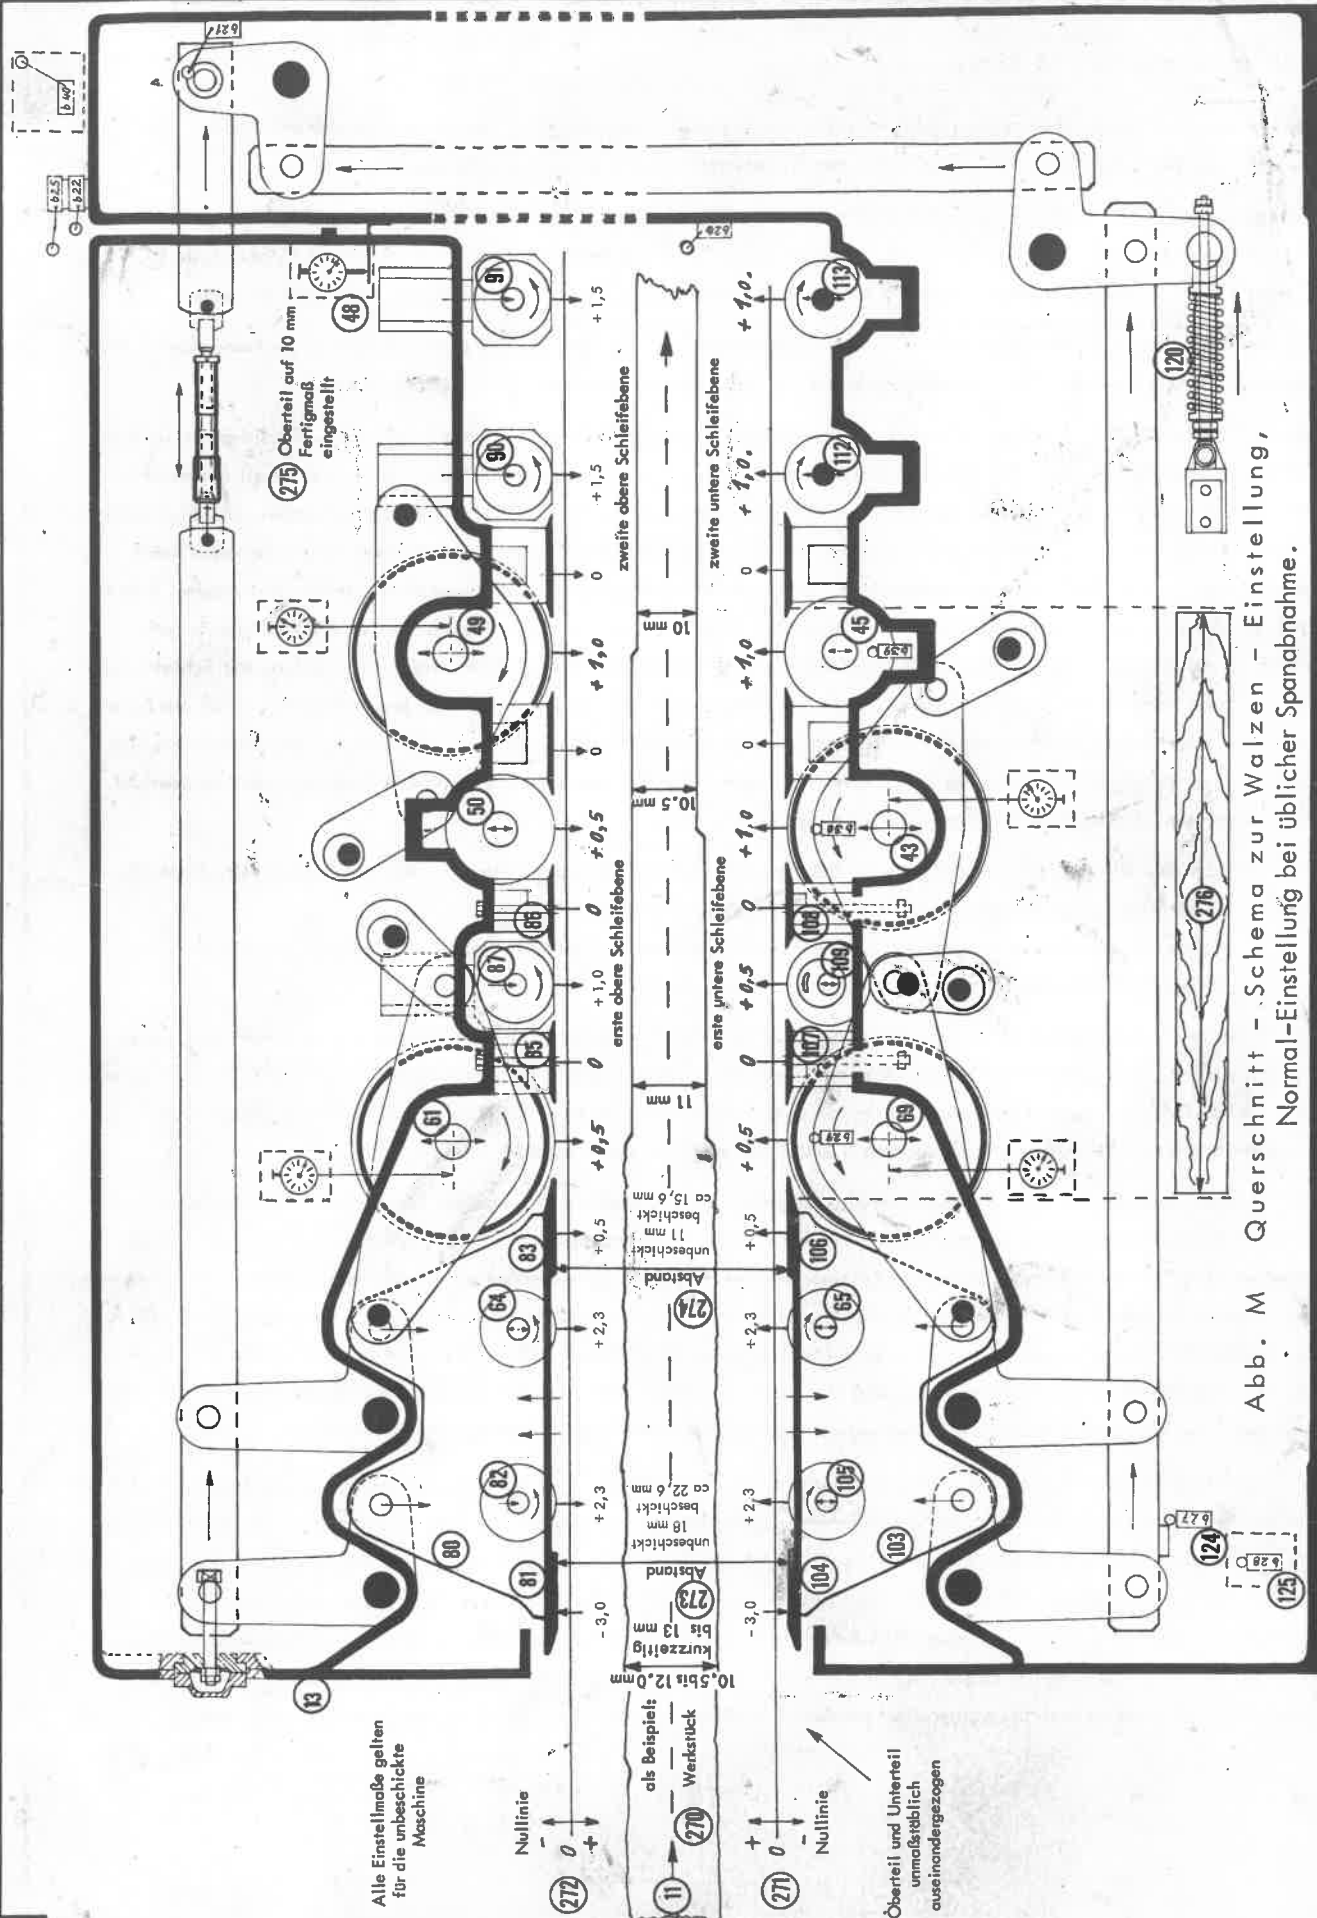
Abb. M Querschnitt - Schema zur Walzen - Einstellung,
